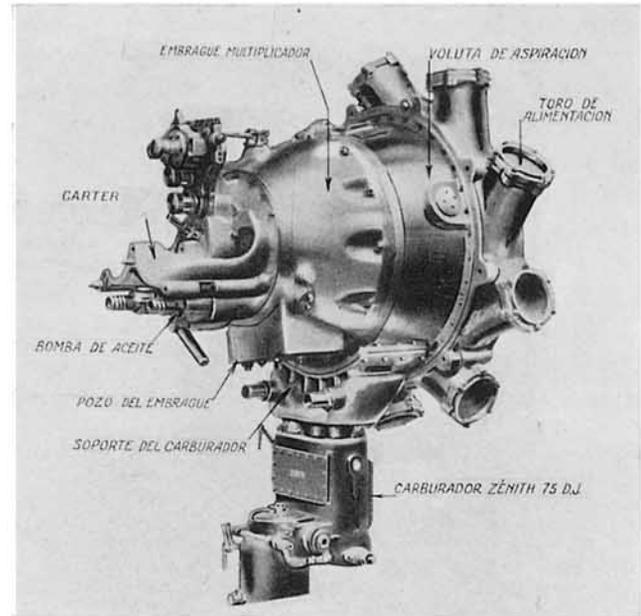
Compresor de mando mecánico para motor en estrella Siemens & Halske de 420 cv.
